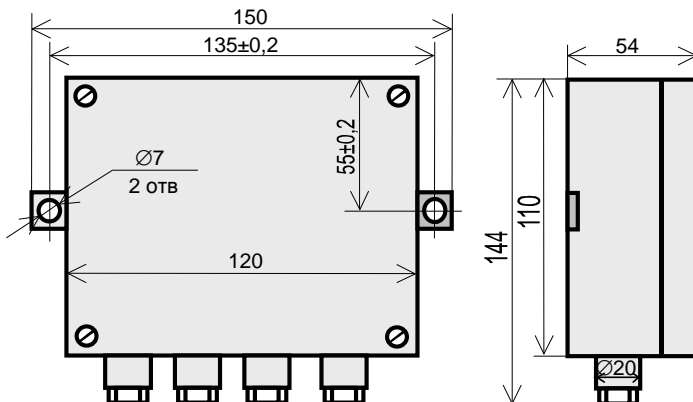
Габаритные и присоединительные размеры КБК и разветвителя
